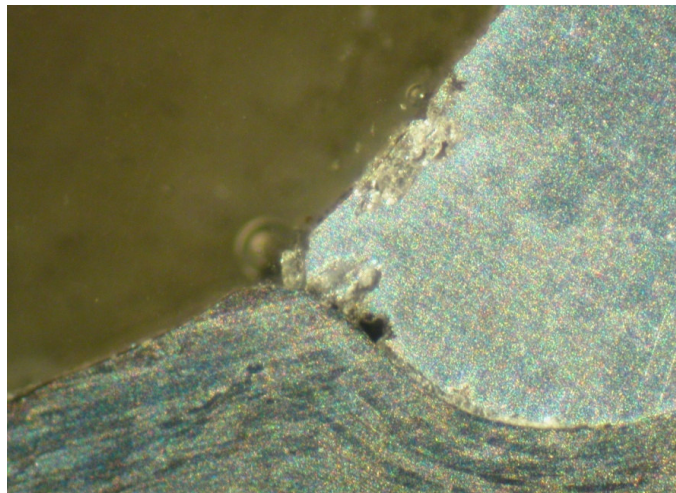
Ingrandimento 6.3x, provino precaricato e lucidato. *Advancing side*, lato superiore, lato di afferraggio. Corrosione per *pitting* sullo *stringer*.
